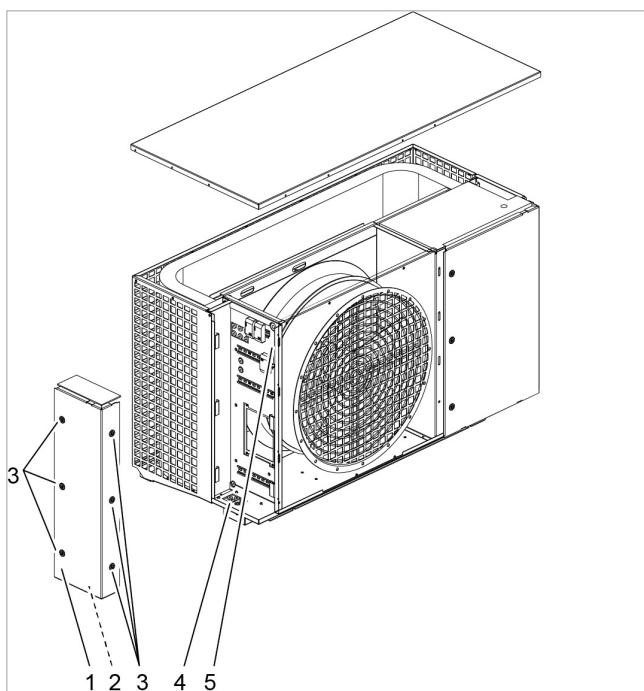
Deckel entfernen und Kabeleinführbogen anschrauben
